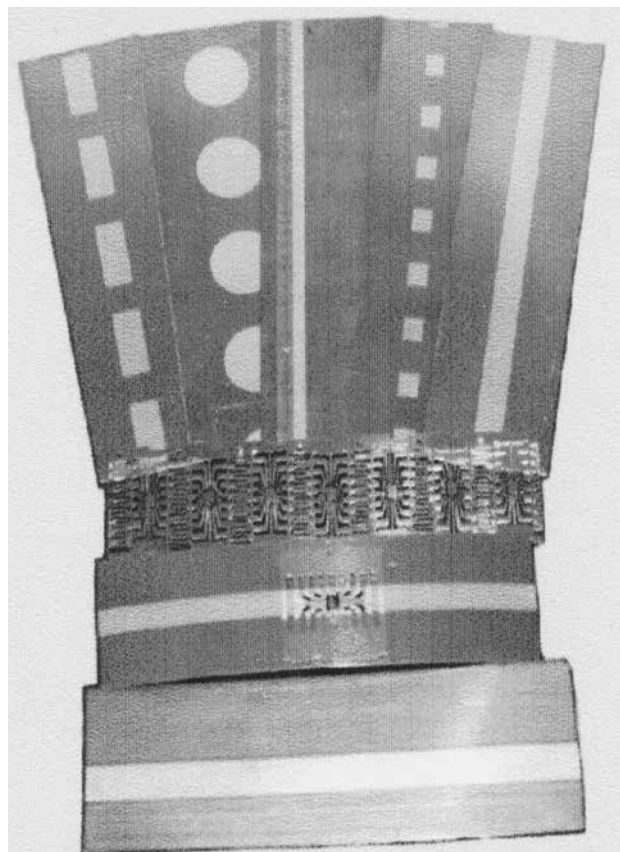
Образцы кадровых отрезков ИС и их заготовок
